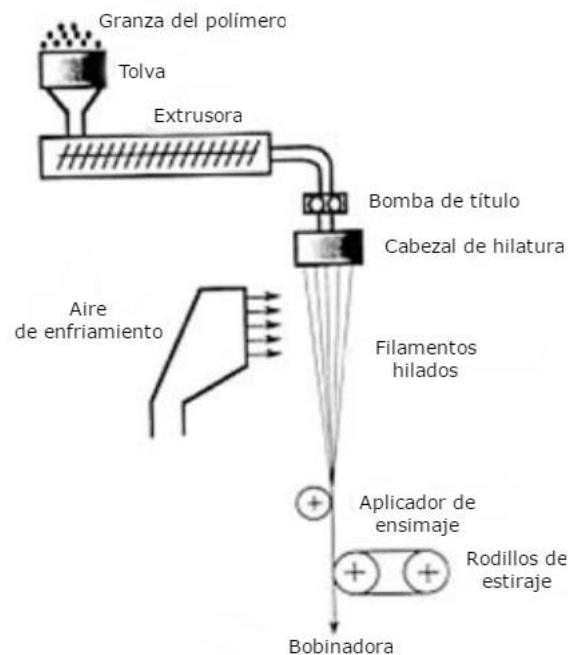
Diagrama de la planta piloto de extrusión multifilamento
